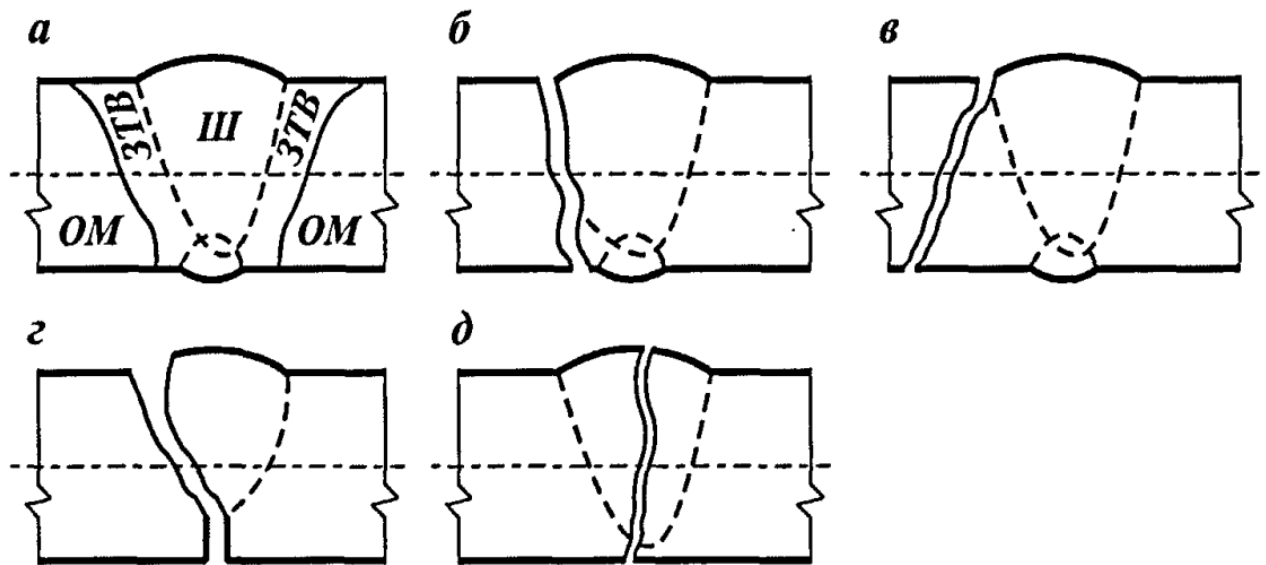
Основные схемы разрушения сварных швов [47]:
